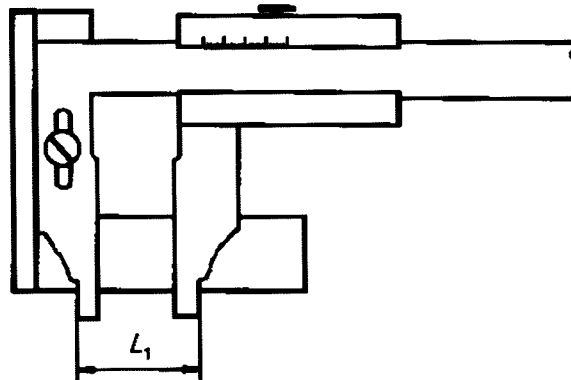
Інструмент для вимірювання  $L_1$  деталь рис. А.8
